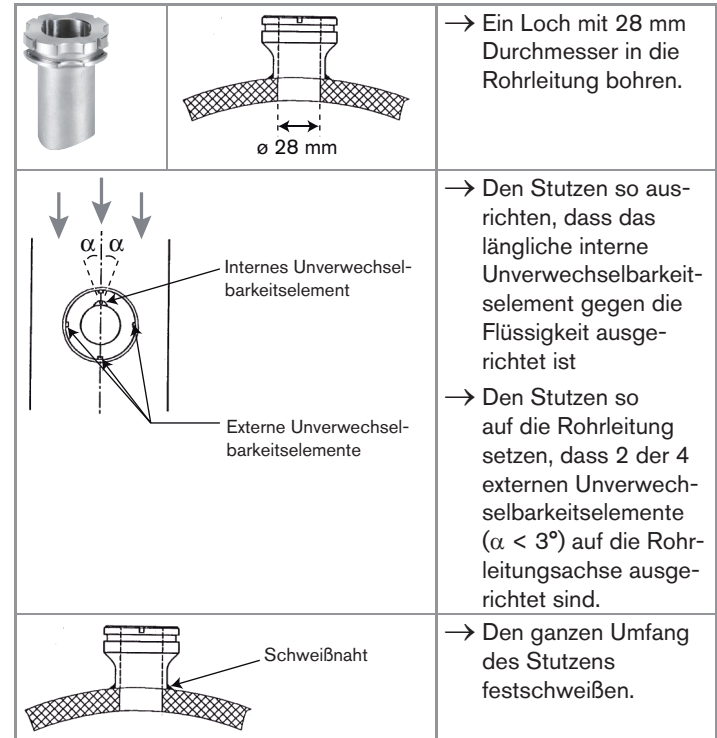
Installation eines Schweißstutzens aus Edelstahl
